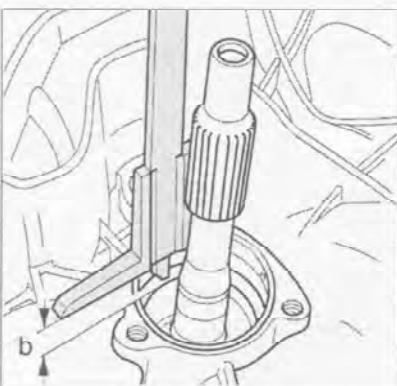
Штангенциркулем измерьте расстояние *b* до поверхности шарикоподшипника.
